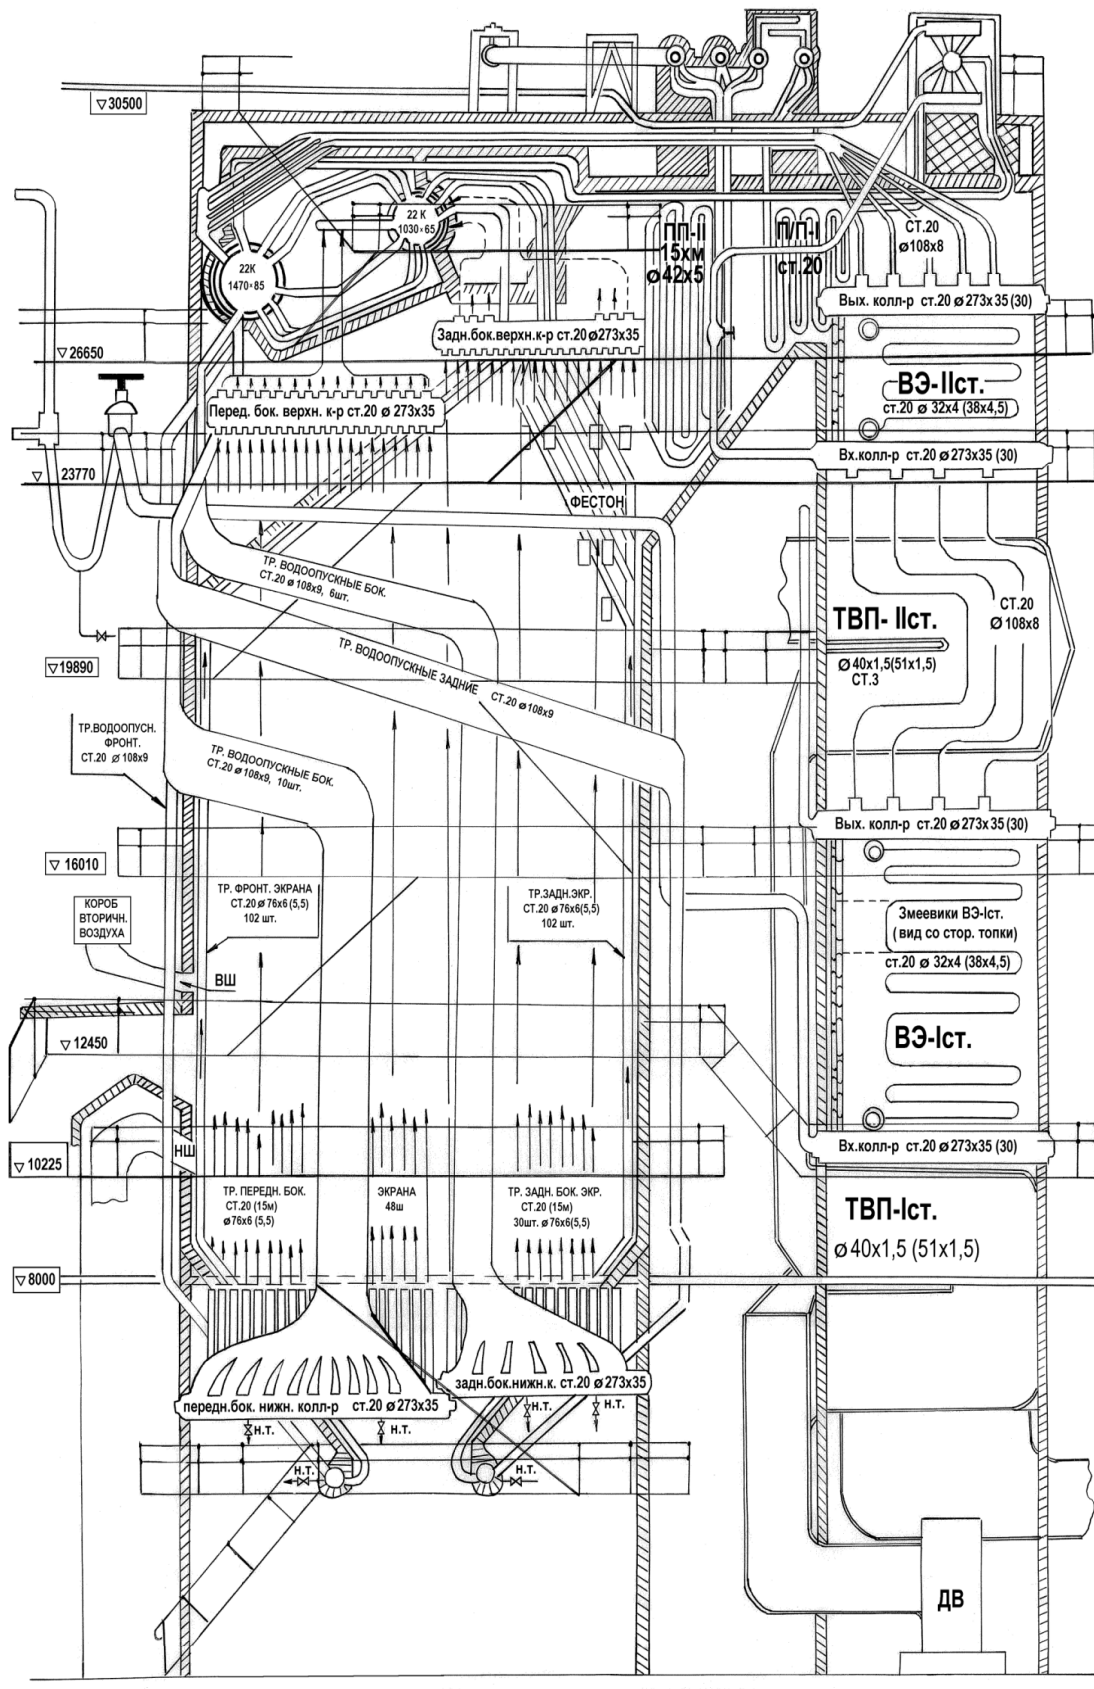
Схема устройства котлоагрегата ПК – 14[14]
